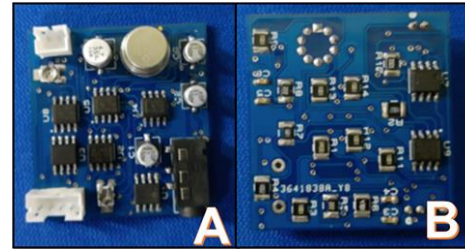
Armado de PCB A) Cara superior y B) Cara inferior
